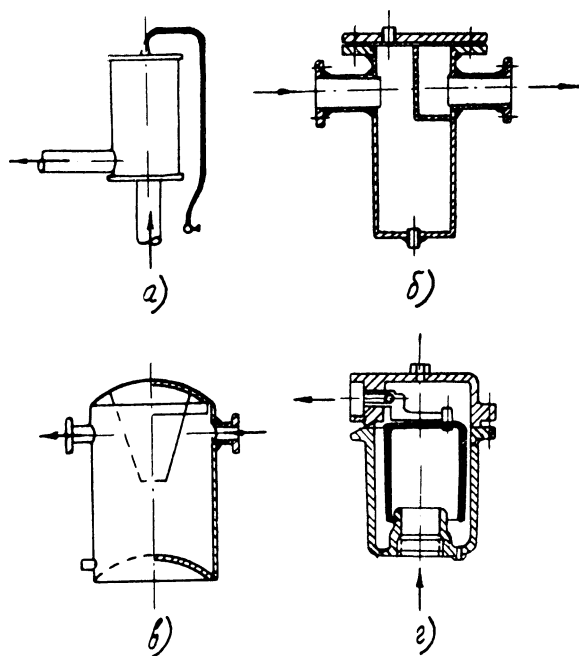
Специальные виды арматуры для трубопроводов котельных установок:
